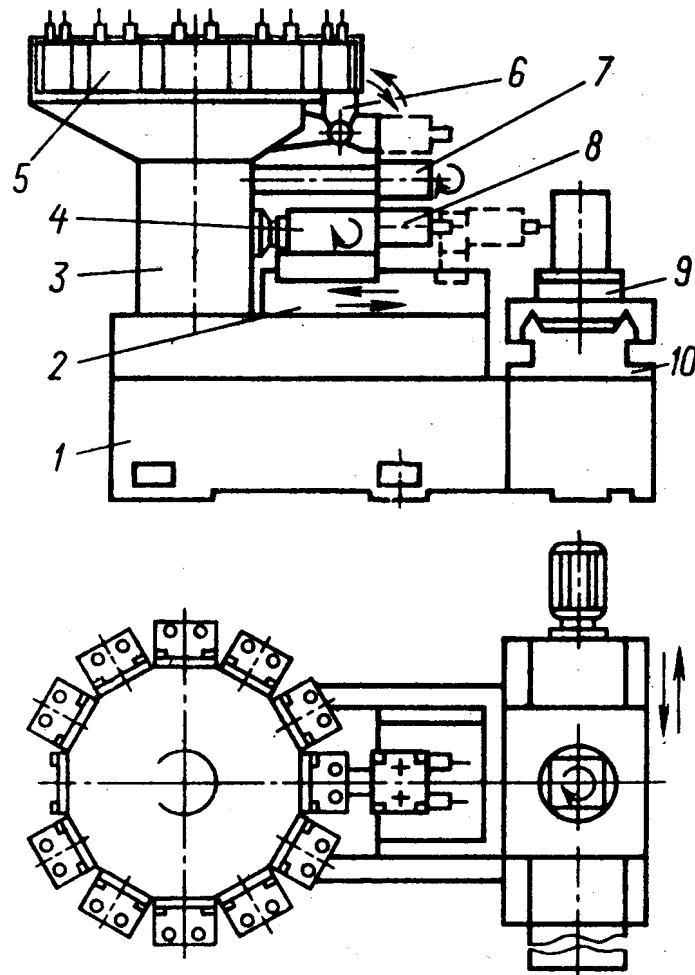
Переналагоджуваний багатоопераційний верстат з ЧПК зі змінними багатошпindelними коробками
